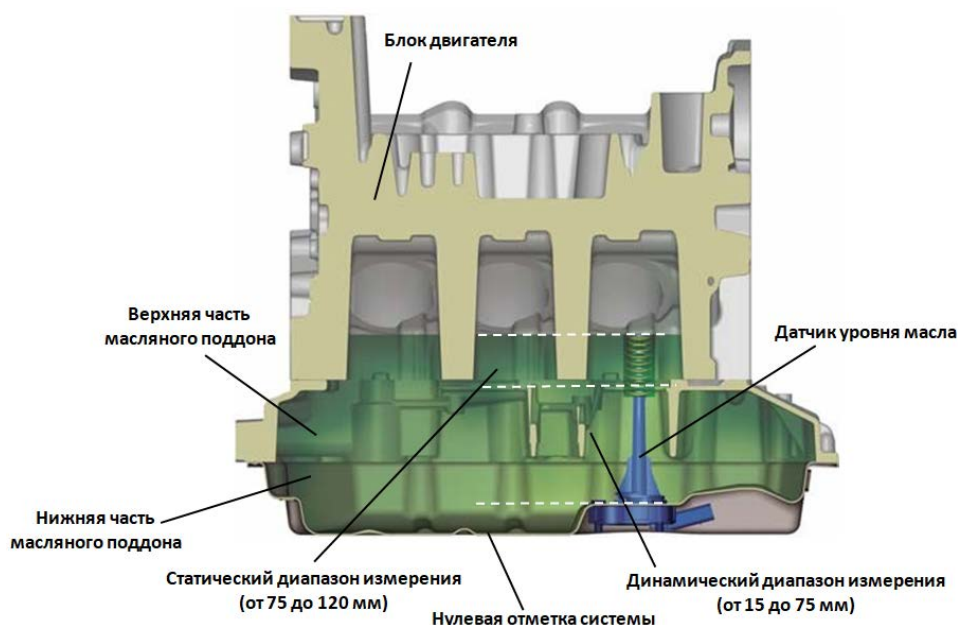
Поперечный разрез блока цилиндров двигателя с отметками уровня масла
